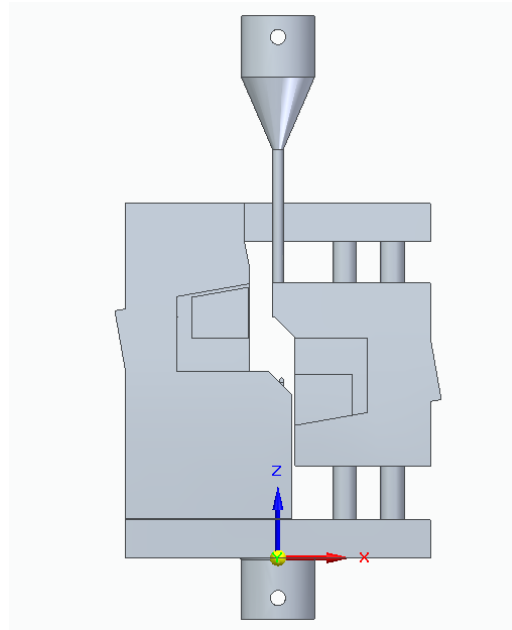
Segundo diseño del utillaje para ensayo de Iosipescu
